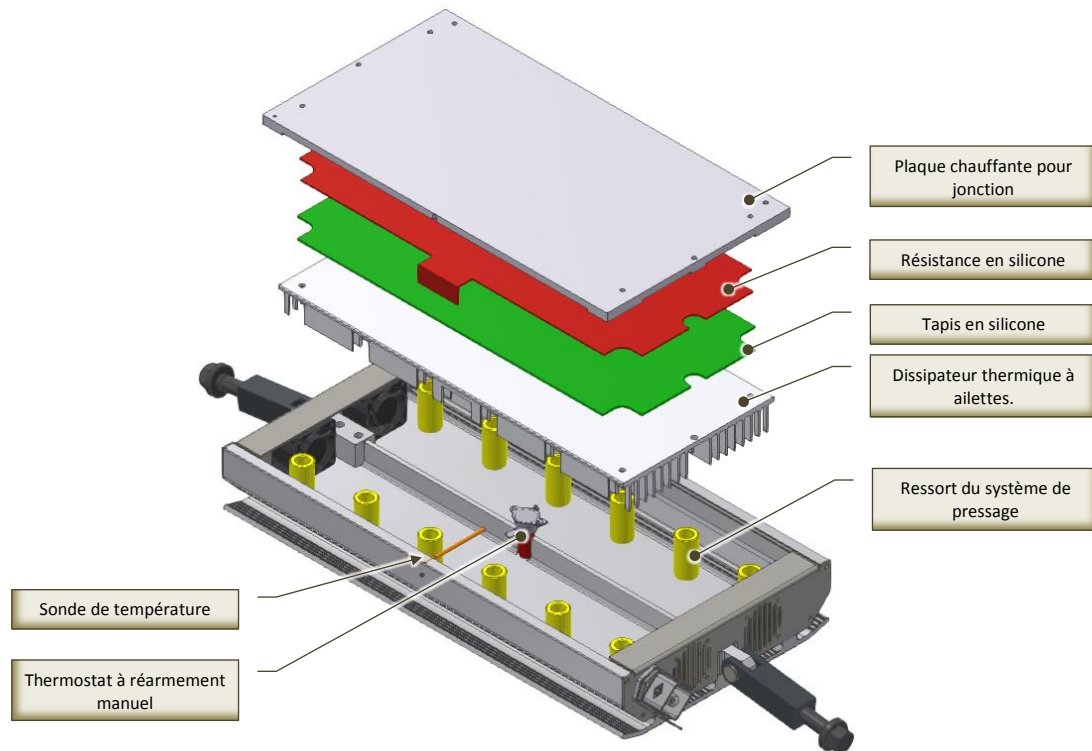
Vue éclatée du plateau inférieur de la presse
